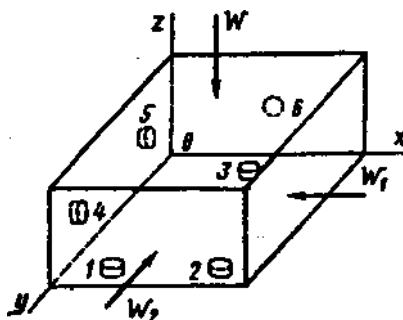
Схема базування оброблюваної деталі в пристрою по шести опорних точках
